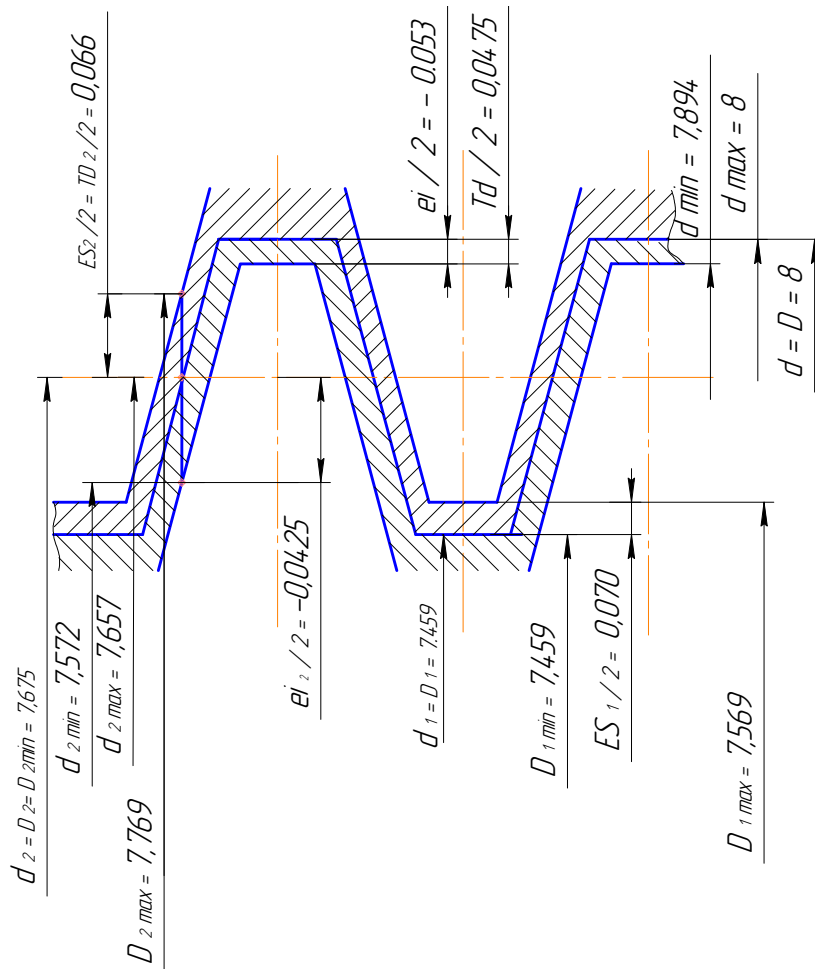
Схема розташування полів допусків для різбового з'єднання із зазором
